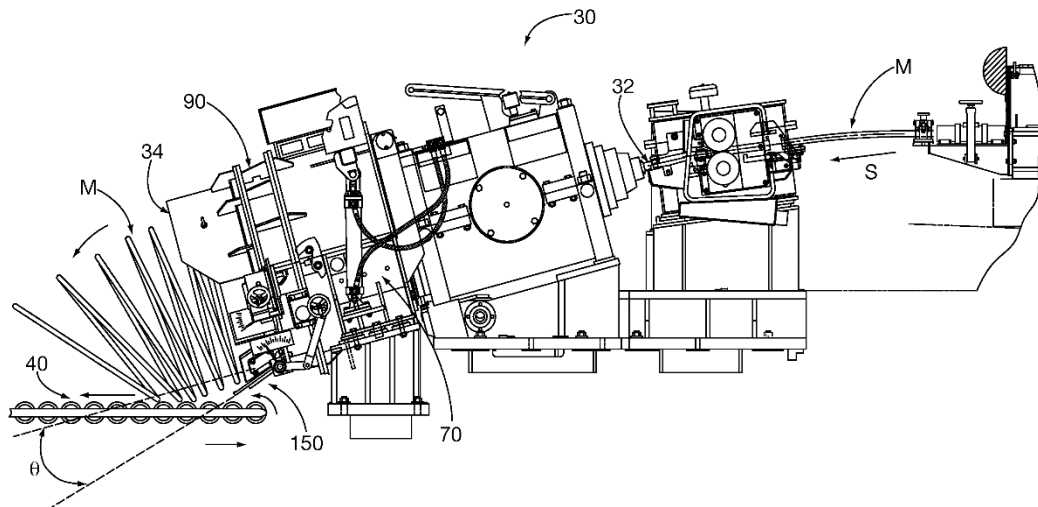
Загальний вид виткоутворювача проволочного стану
